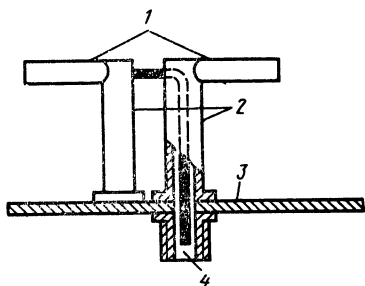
Конструкция схемы вибраторного излучателя:
